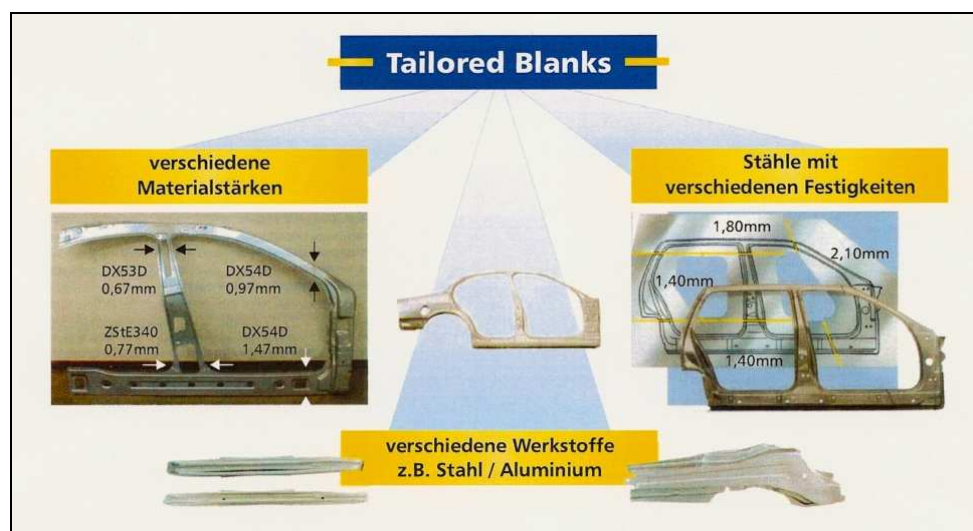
Schweißbare Werkstoffe (Thyssen Krupp Steel)
